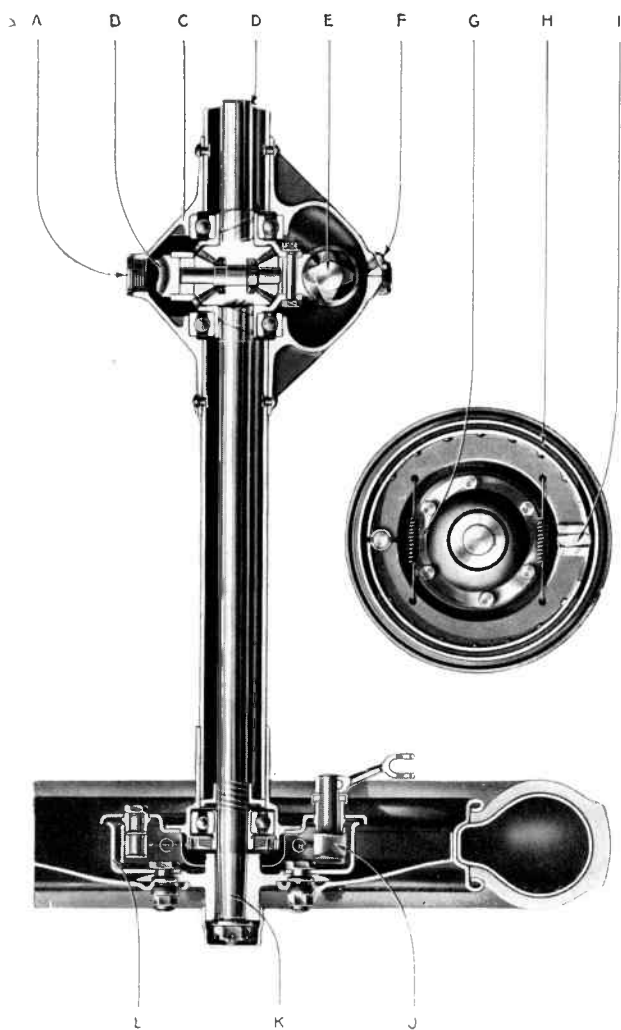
Coupe du pont arrière et vue d'un frein.
